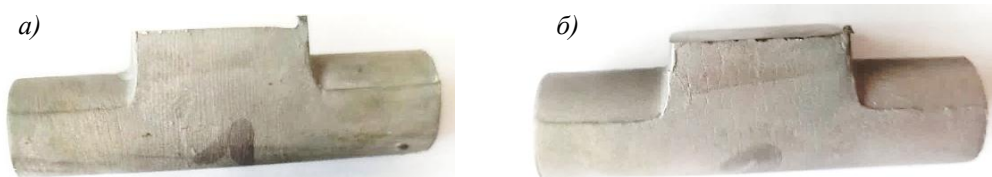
Литые заготовки из сплавов ВЖЛ220 (а) и ВЖЛ718 (б)
